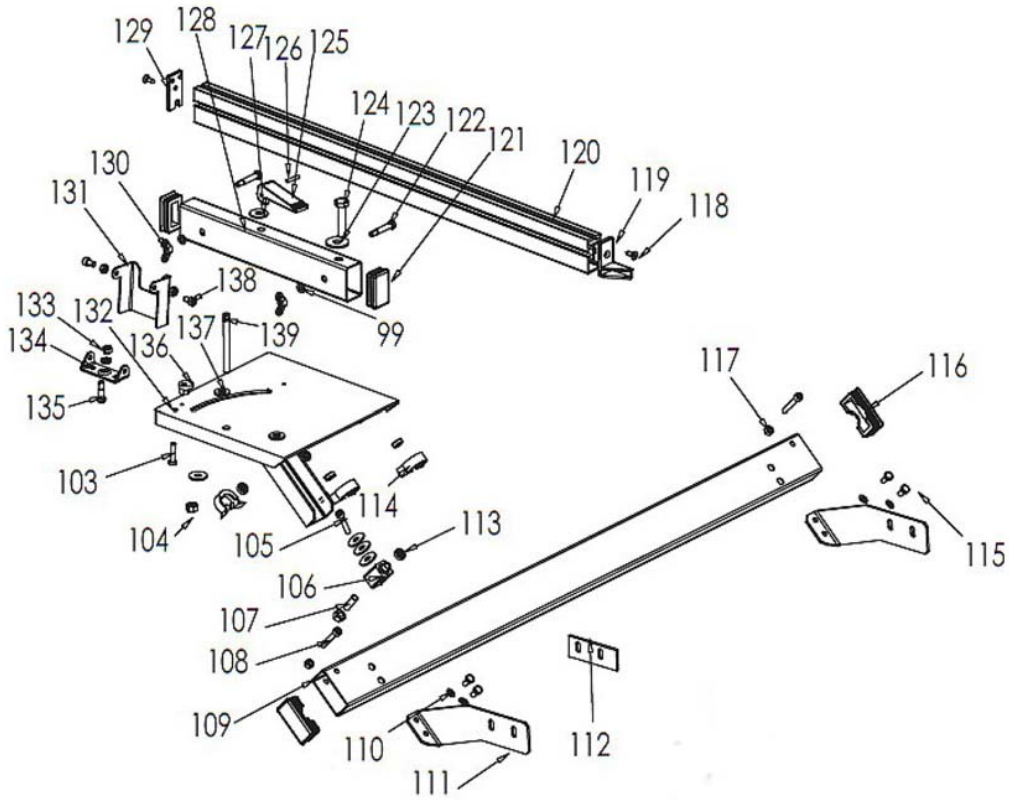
Vue éclatée 2 : Plateau coulissant
